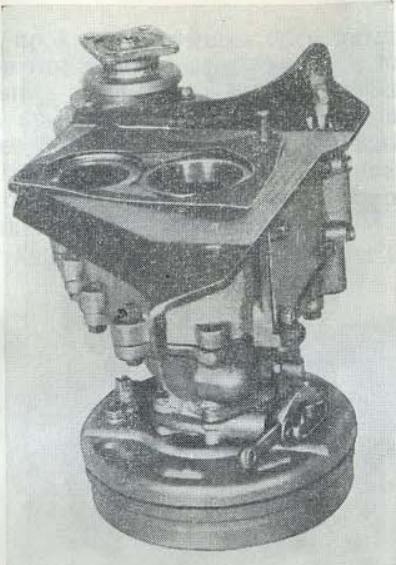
Раздаточная коробка, подготовленная для соединения с коробкой передач
